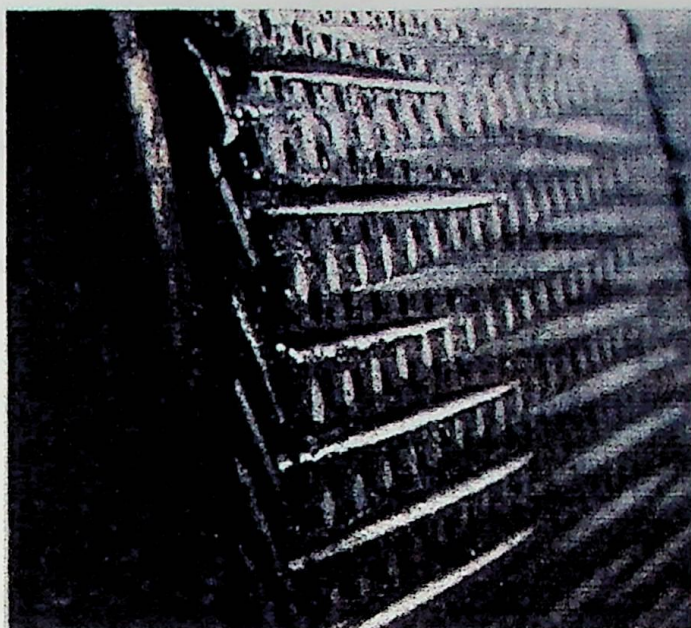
Superfície do corpo de prova usinado com ferramentas de corte de metal duro ISO K10 ($a_p = 1,0$ mm, $f = 0,1$ mm/volta, $V_c = 900,8$ m/min).
